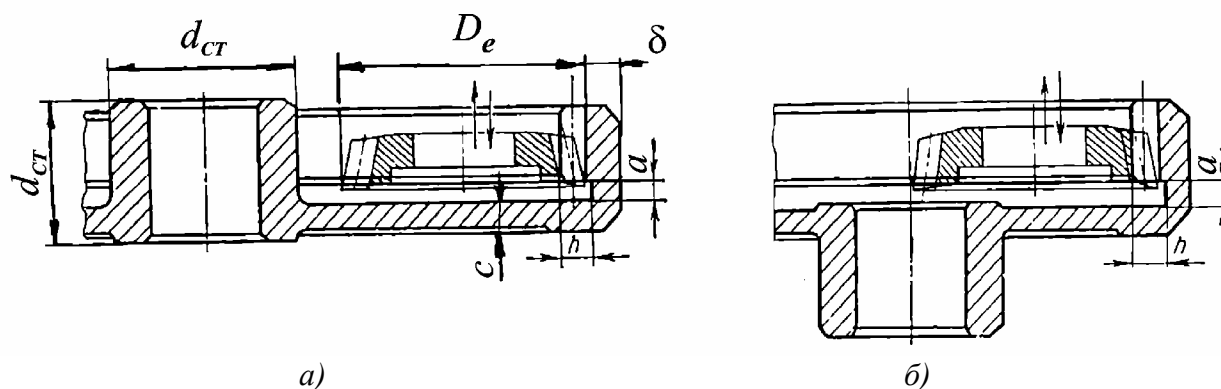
Конструкции цилиндрических зубчатых колес внутреннего зацепления
